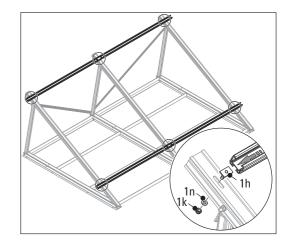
Montaggio delle guide dei profili di montaggio, passaggio 2
